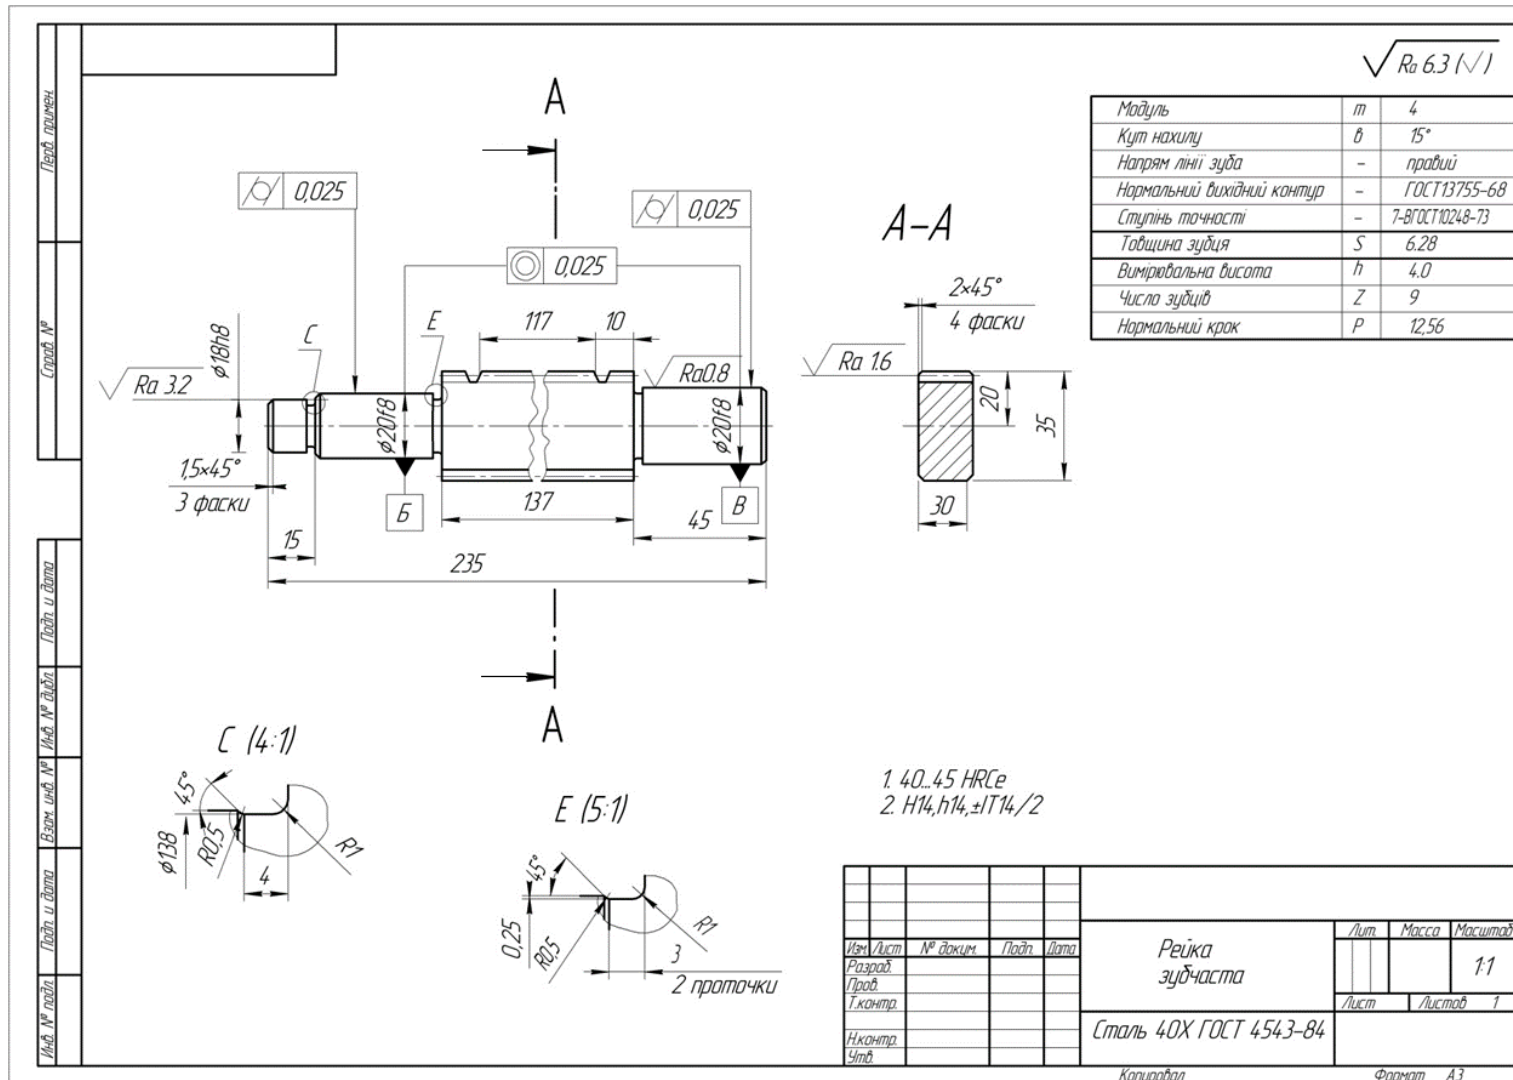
Робочий кресленник зубчастої рейки
